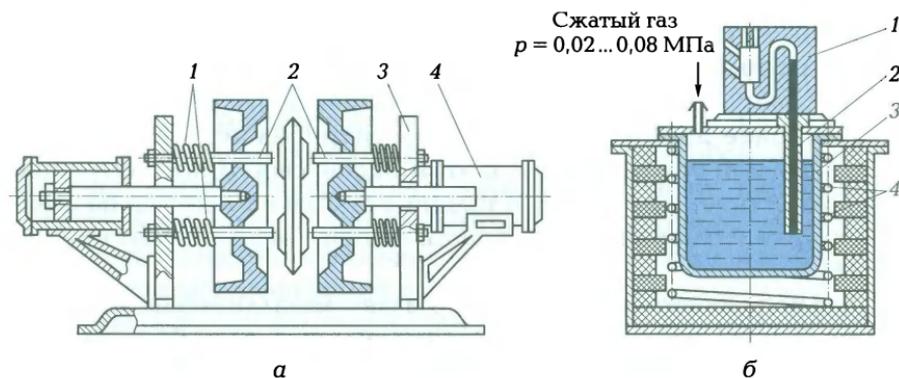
Схемы кокильного станка и установки для заполнения кокилей: а — кокильный станок с пневматическим приводом: 1 — пружины; 2 — толкатели; 3 — плита; 4 — пневматический привод; б — установка для литья под низким давлением: 1 — кокиль; 2 — металлопровод; 3 — тигель; 4 — электронагреватель
